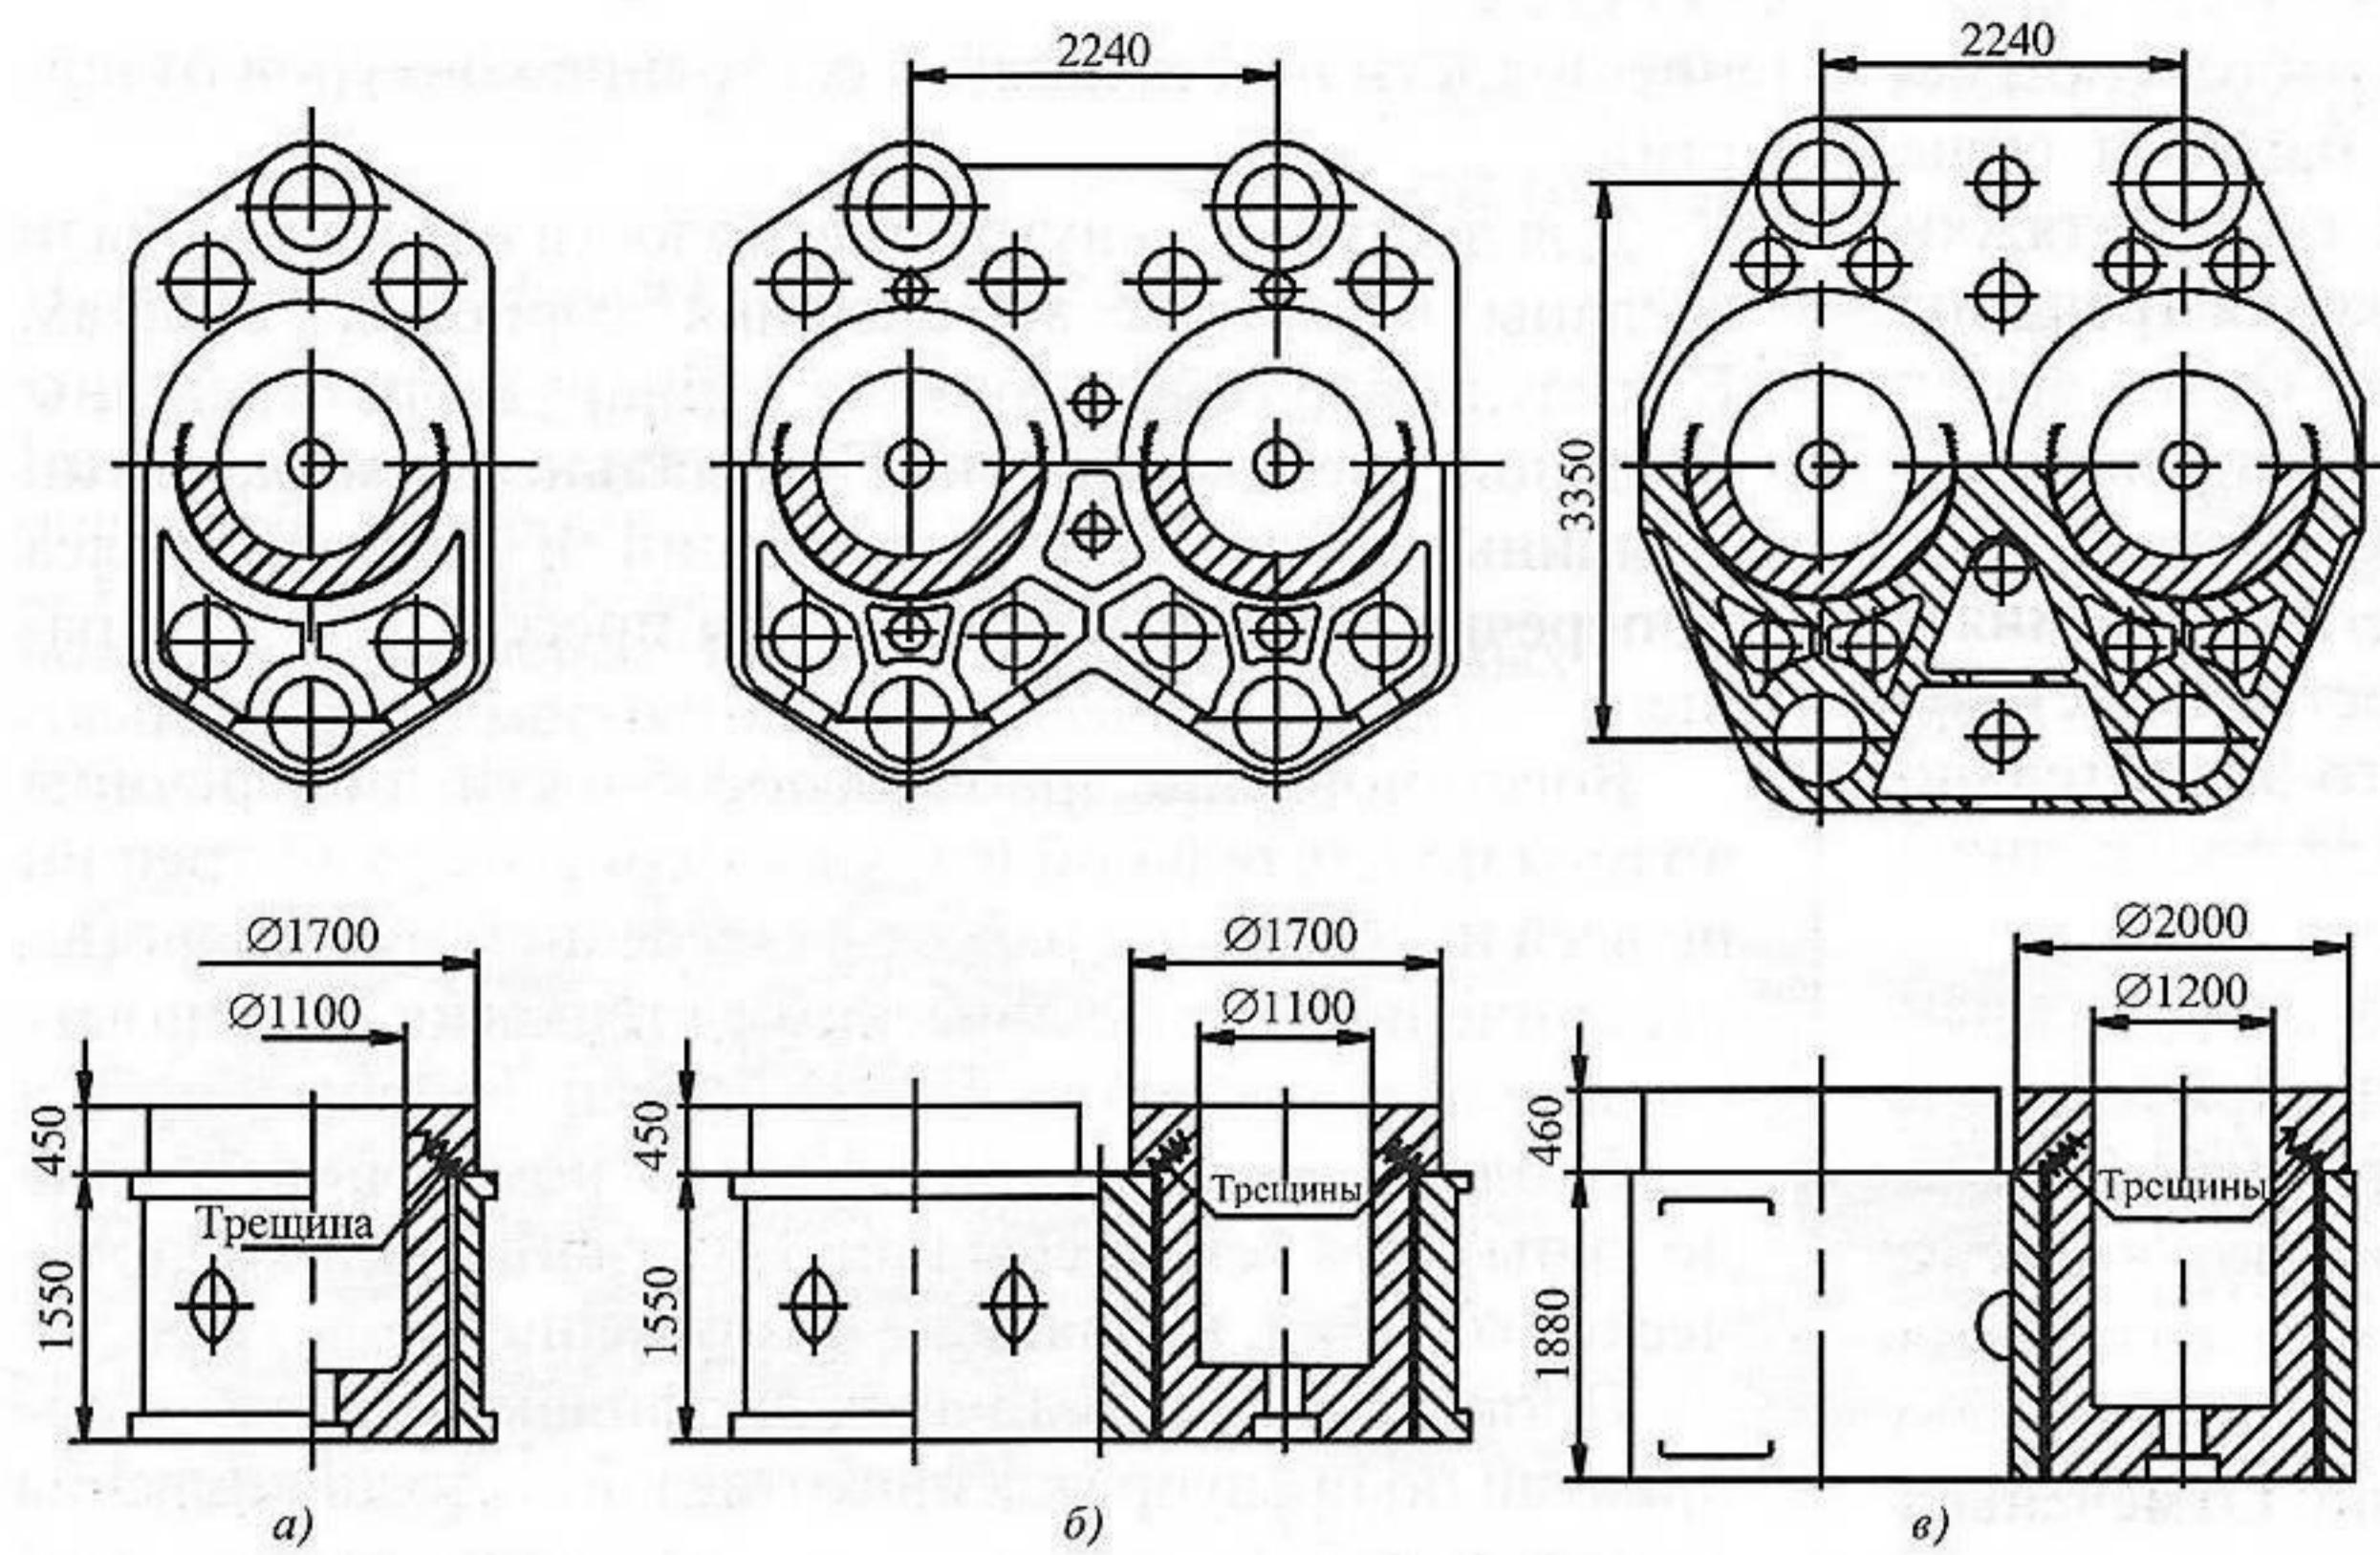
Разрушение цилиндров прессов для формовки заготовок труб диаметром 1020...1220 мм:
